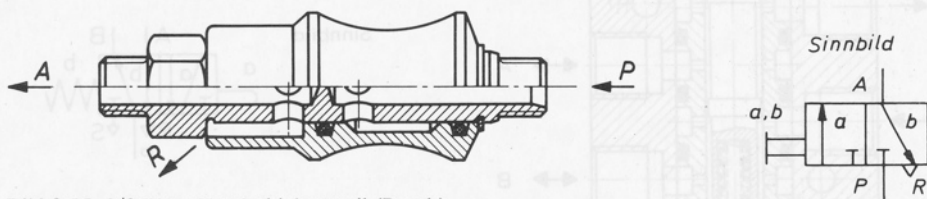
3/2-Wege-Handschiebeventil (Bosch)
